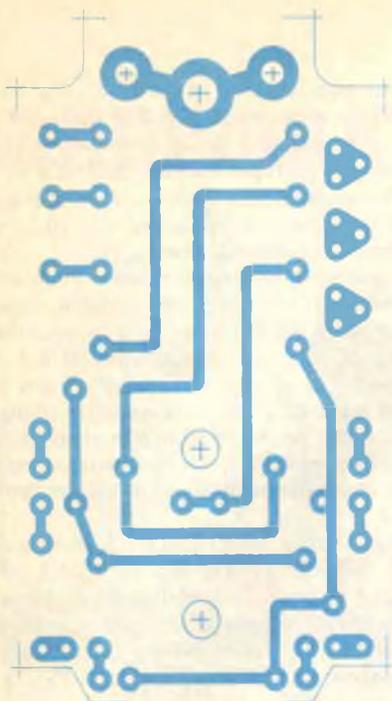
A sinistra in alto è illustrato il circuito stampato principale ed a destra è indicata la disposizione dei componenti. Il circuito stampato qui a lato è per il commutatore rotante.
